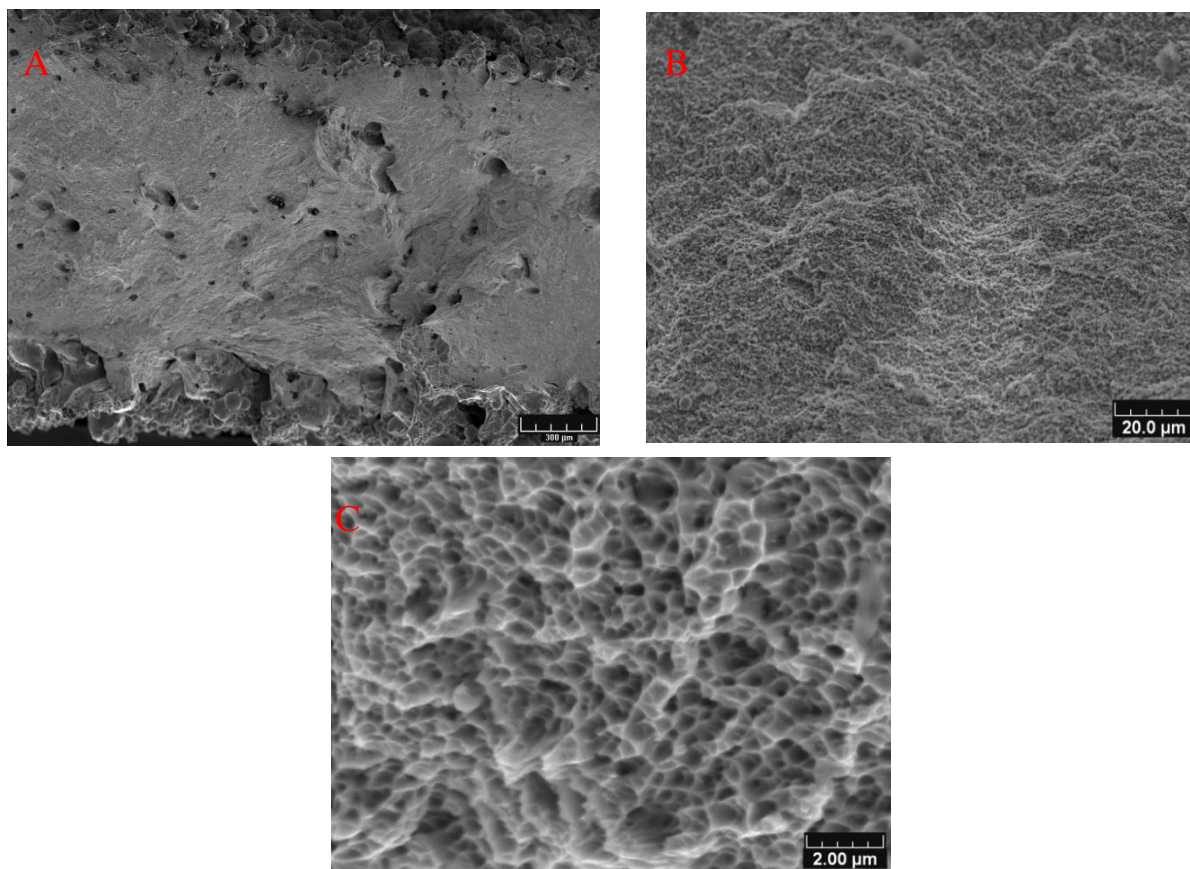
Morphologie de la fracture des éprouvettes selon la position B de construction.
